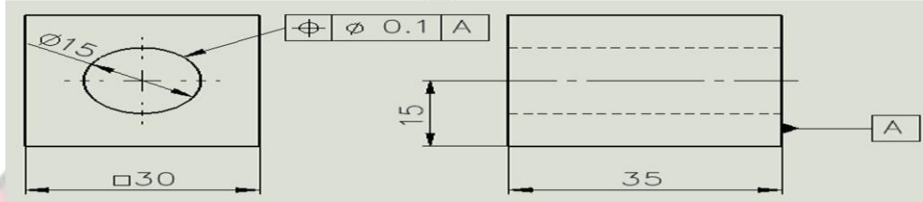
การเรียกใช้งานคำสั่ง Geometric Tolerance
